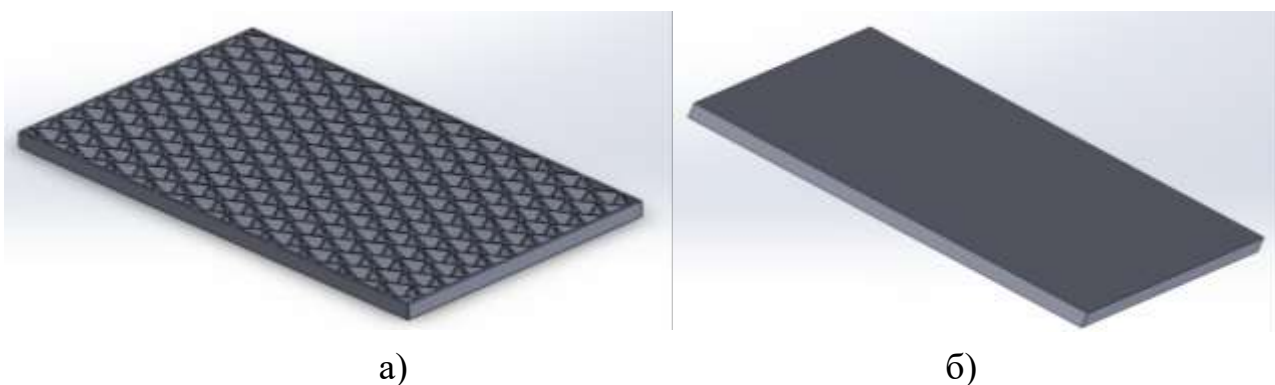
Зразок виготовлений із матеріалу EVA: а) поверхня з нерівностями; б) гладка поверхня
